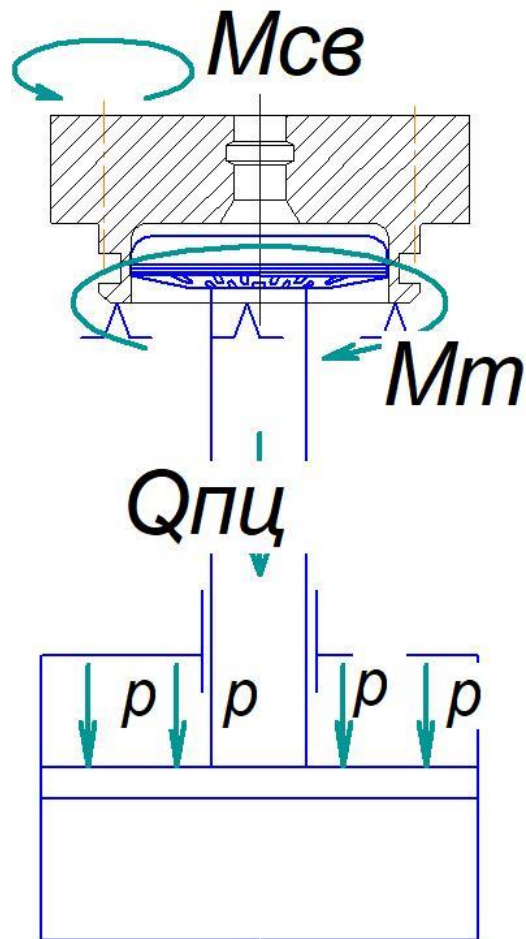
Розрахункова схема пристрою для п'ятикоординатного верстата
